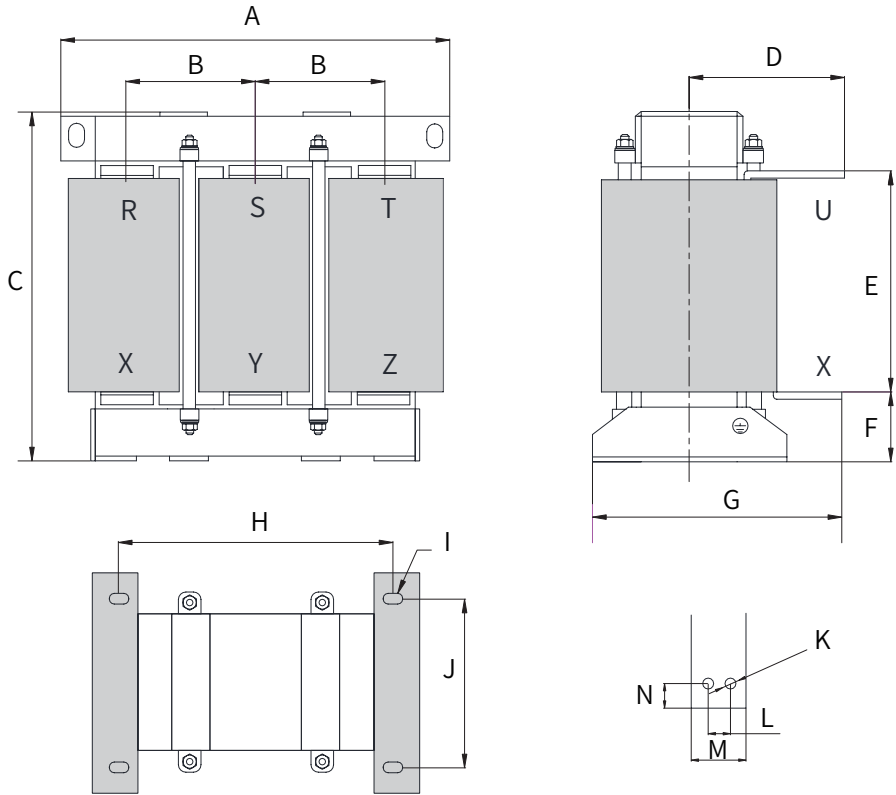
Размеры входного реактора переменного тока 800/1000 А
